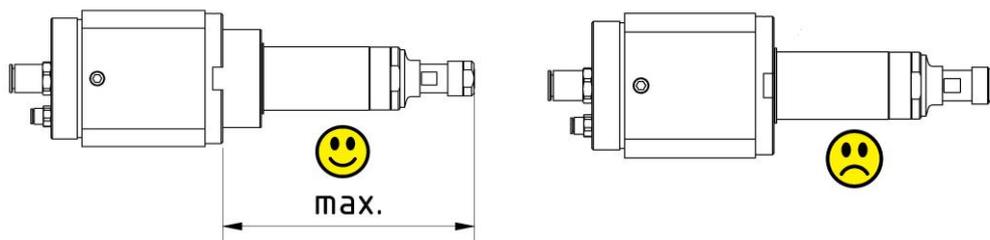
Max. Auslenkung axiale Roboterspindel
